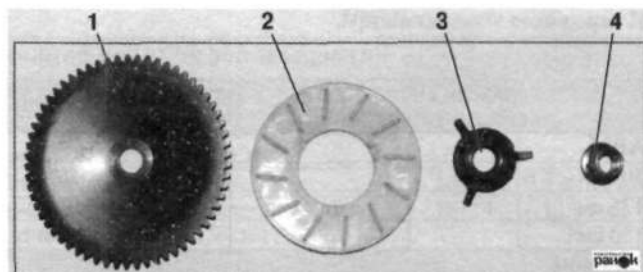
Внешняя половина ведущего шкива: 1 – шкив привода кикстартера (внешняя половина ведущего шкива вариатора); 2 – крыльчатка охлаждения; 3 – втулка храпового механизма; 4 – гайка ведущего шкива вариатора
